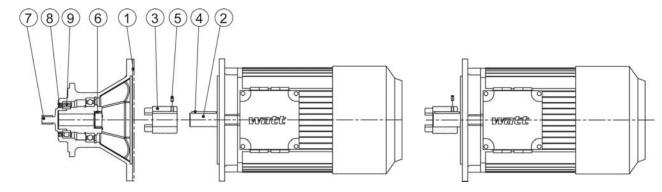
Montage eines IEC – Motors an eine Kupplungsadapter (IAK)
